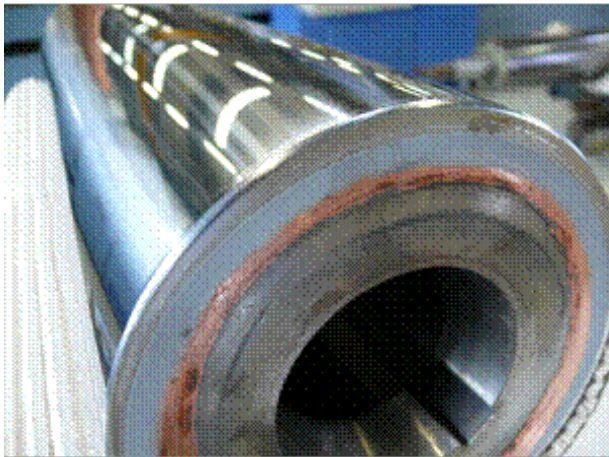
galvanisierter polymerbeschichteter 1800mm Druckzylinder
